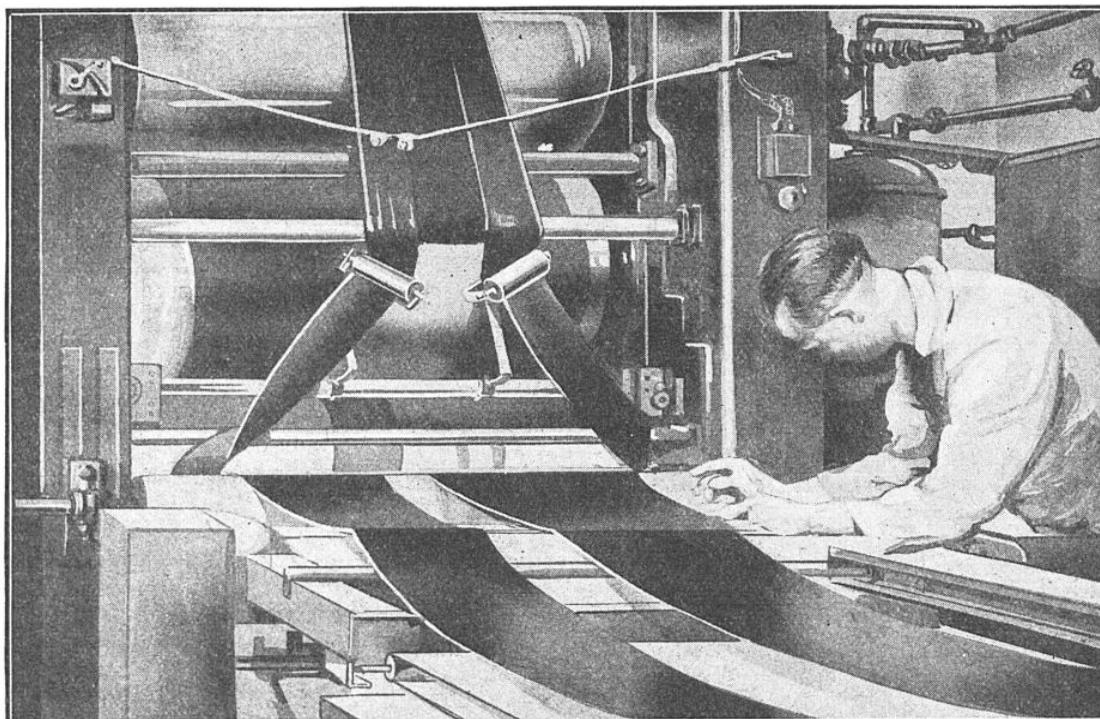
FABRICATION DES CHAPES, OU BANDES DE ROULEMENT, D'UN PNEUMATIQUE
